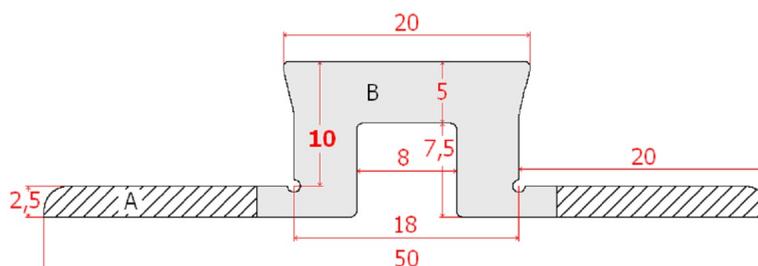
BS PROFILE H10 in sezione (dimensioni in mm)
